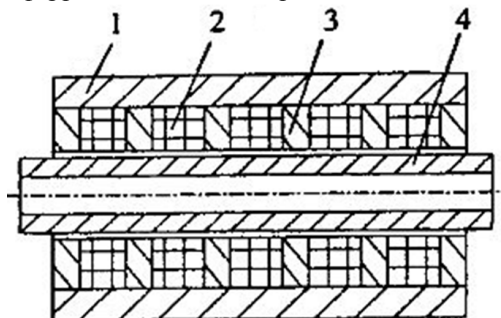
Цилиндрический (коаксиальный) линейный двигатель
